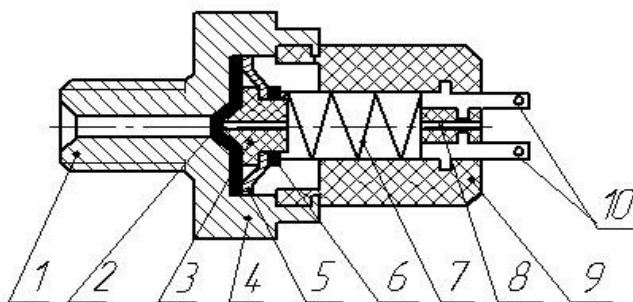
Датчик давления масла типа ММ-120: 1 – стальной корпус; 2 – диафрагма из полиэфирной пленки; 3 – пластмассовый толкатель; 4 – шестигранник под ключ; 5 – неподвижный электрический контакт; 6 – подвижный электрический контакт; 7 – цилиндрическая пружина; 8 – пластмассовая вставка; 9 – отверстие с пробкой-фильтром; 10 – штекеры
